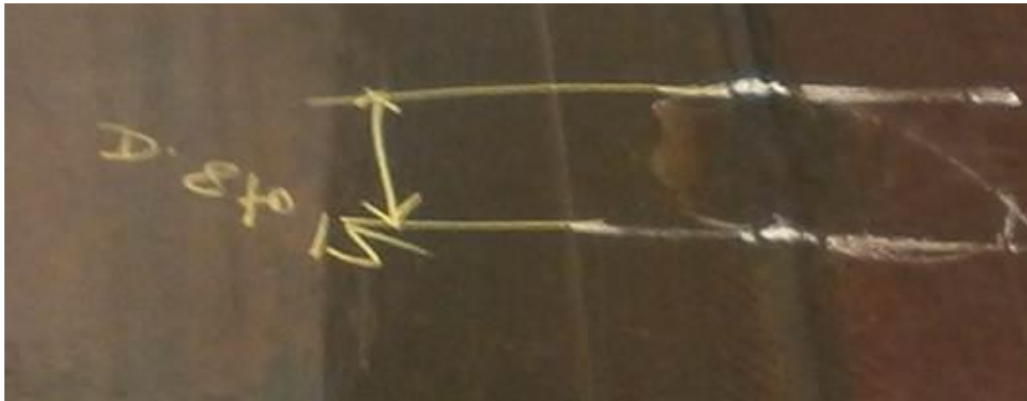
Marcado de una soldadura defectuosa [9]
